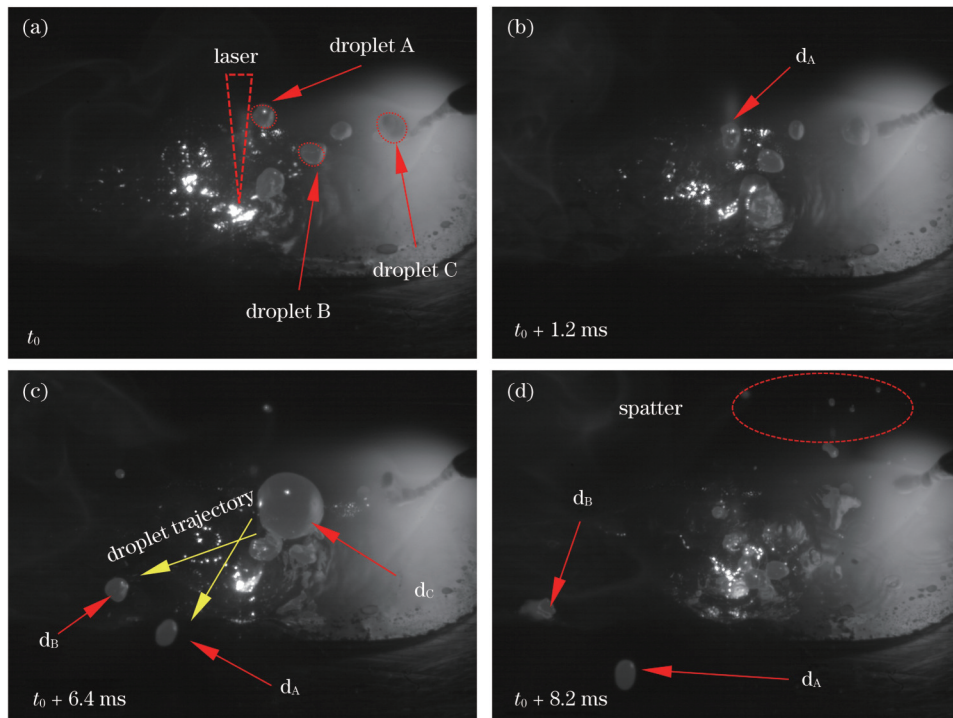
焊接过程高速摄像照片(5# 试验)
